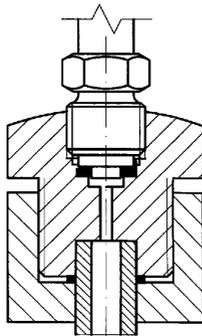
Zylindr. Gewinde, Abdichtung mit Dichtung an Dichtfläche
